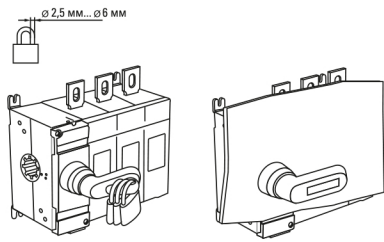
Установка рукоятки управления прямой установки 315-1600А
